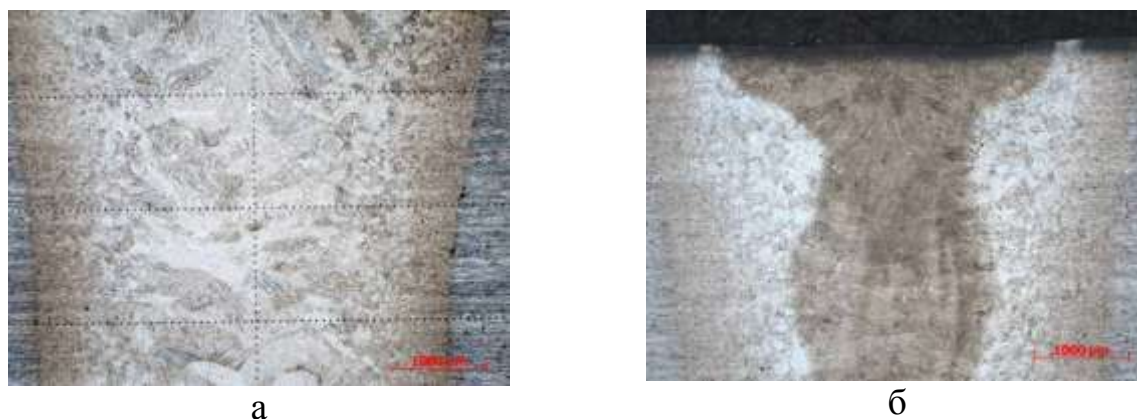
Общий вид сварных швов ВТ20:
